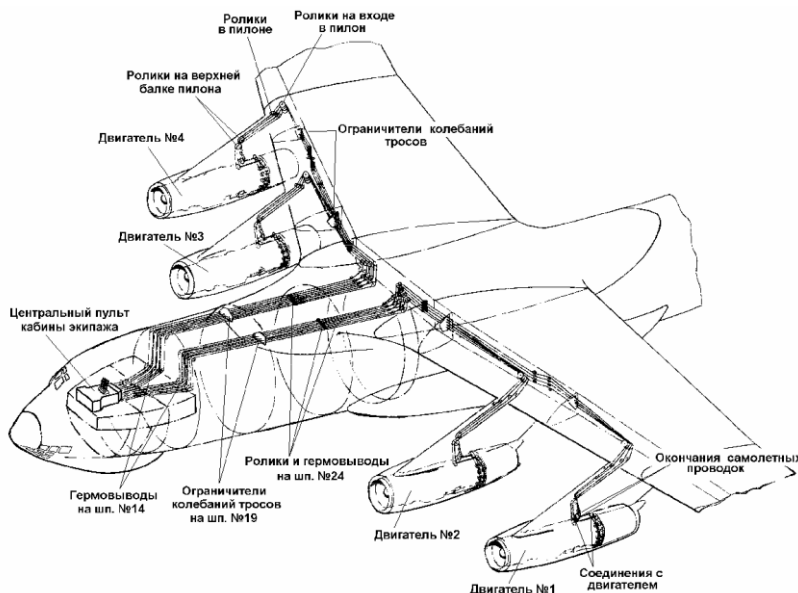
Система управления двигателями самолета Ил-76ТД
